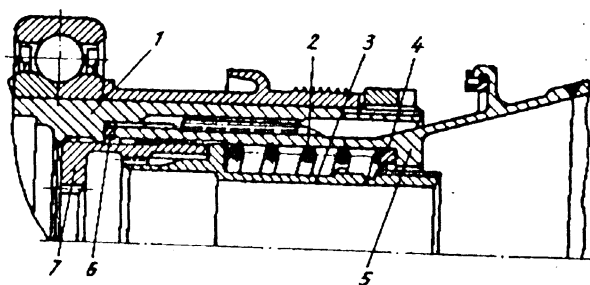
Узел соединения роторов компрессора и турбины компрессора:
